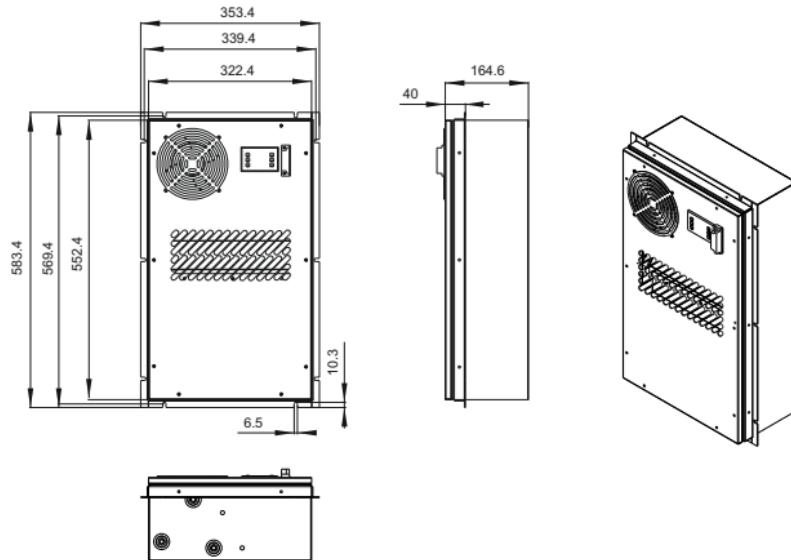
Внешний вид и габаритные размеры модели СМ-0300-230 / Figure 1 – Appearance and overall dimensions of CM-0300-230 version
